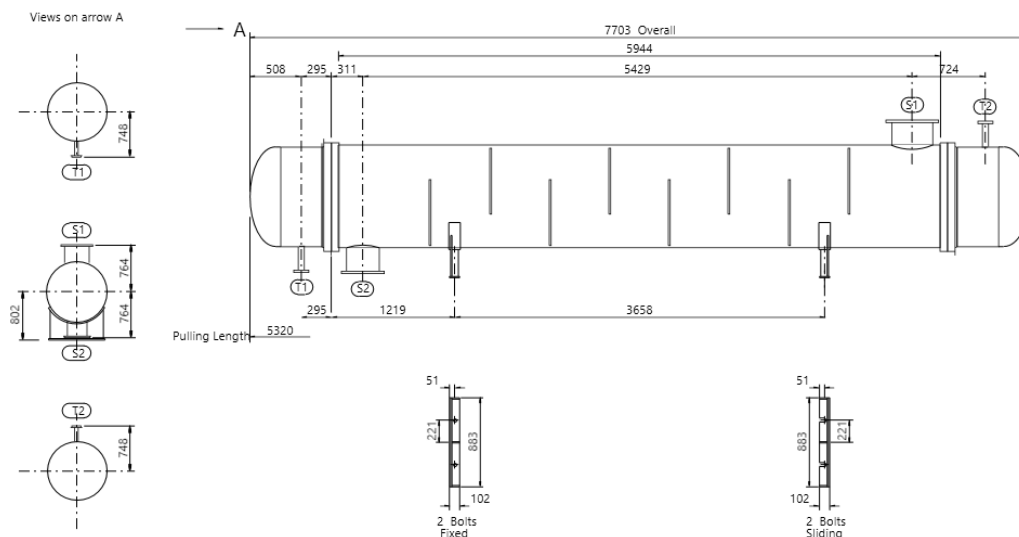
Геометрические размеры кожухотрубчатого теплообменника из Aspen EDR *Fig. 4. Geometric dimensions of the shell and tube heat exchanger from Aspen EDR
